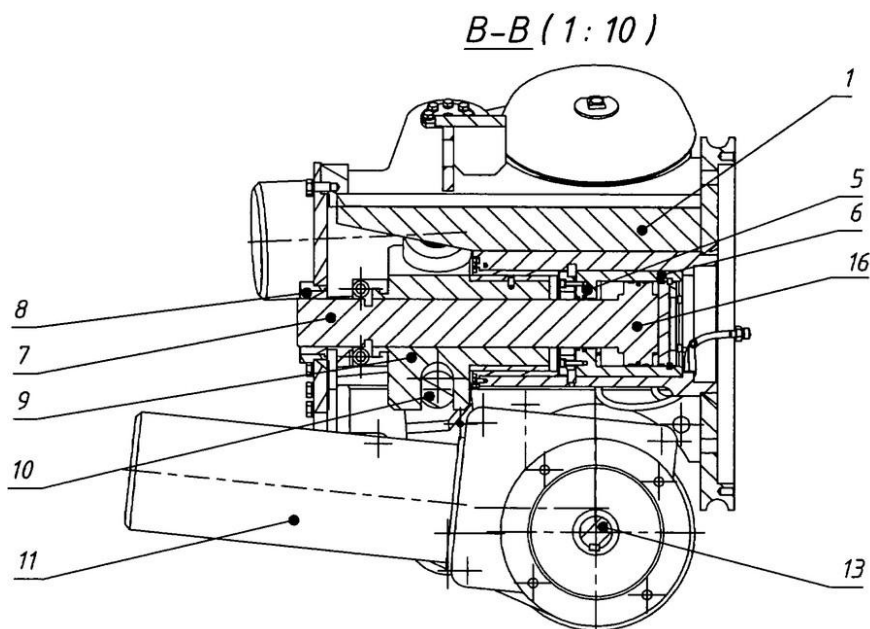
Механизм перемещения машины для сварки труб, в дальнейшем "механизм перемещения", сечение В-В
